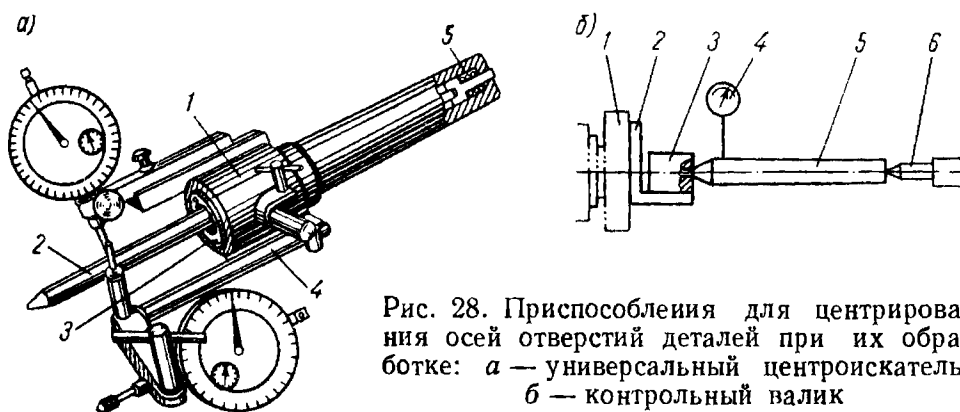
Приспособления для центрирования осей отверстий деталей при их обработке: а — универсальный центроискатель; б — контрольный валик
